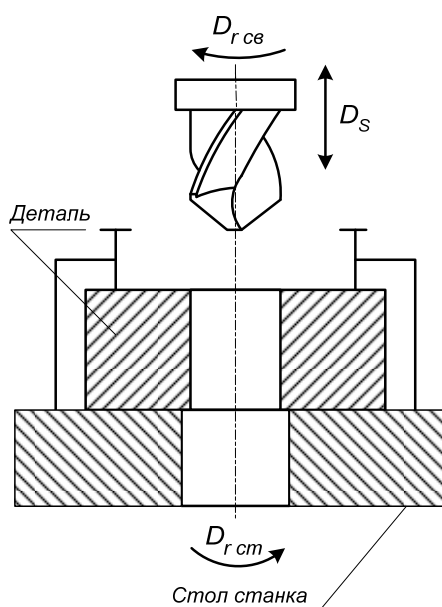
Третья схема операции сверления: обрабатываемая деталь и сверло вращаются в противоположных направлениях
